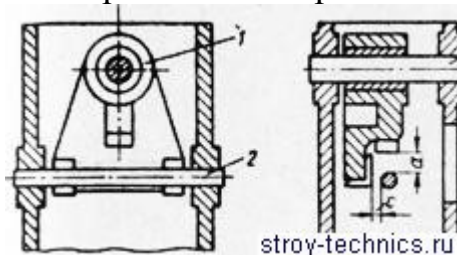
Схема проверки межосевого расстояния и правильности положения валов в корпусе червячного редуктора 1 — скоба; 2 и 3 — оправки
